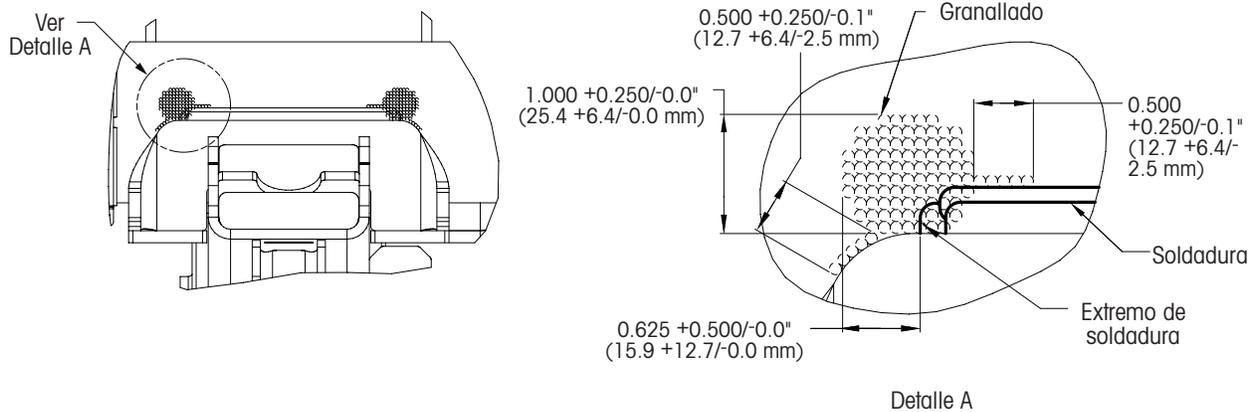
Detalles de granallado de soldadura de eje a viga
